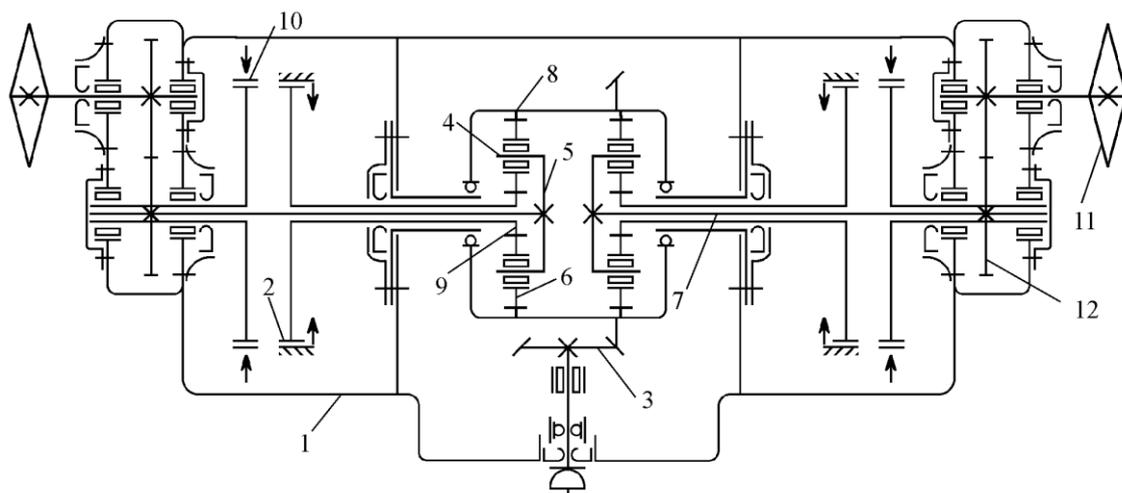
Сдвоенный планетарный механизм поворота: 1 – корпус заднего моста; 2 – тормоз солнечной шестерни; 3 – главная передача; 4 – ось сателлита; 5 – водило; 6 – сателлит; 7 – соединительный вал; 8 – коронная шестерня; 9 – солнечная шестерня; 10 – тормоз водила; 11 – ведущая звездочка; 12 – бортовая передача;
